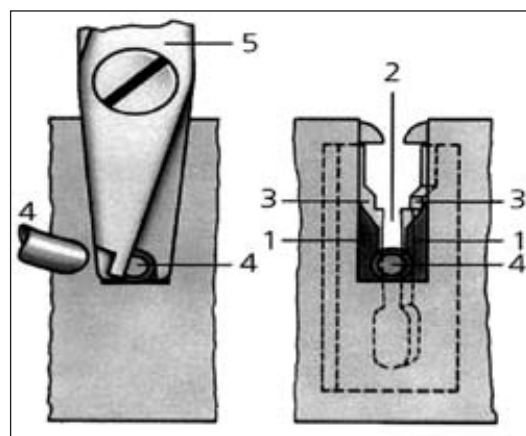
Запрессовка жилы в контакт планта: 1 - Контакты; 2 - Контактный зазор; 3 - Пластмассовые выступы; 4 - Медная жила с изоляцией; 5 - Монтажный сенсорный инструмент
